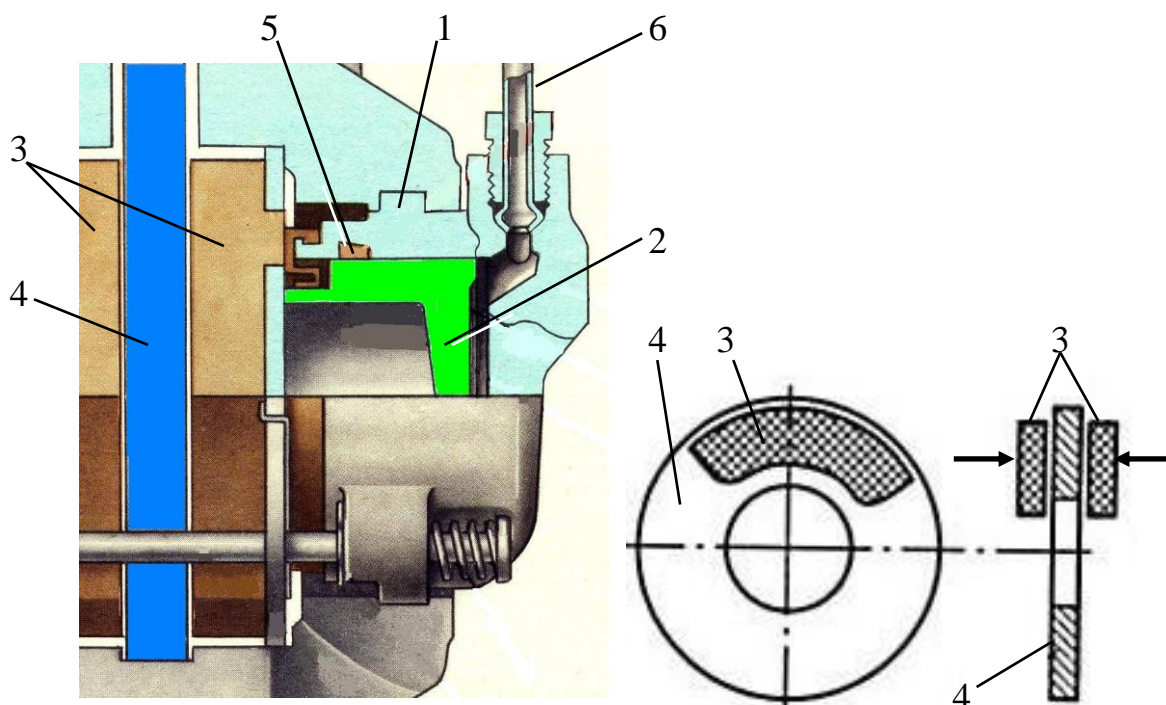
Торможение дискового тормозного механизма: 1 – рабочий цилиндр; 2 – поршень; 3 – накладки тормозных колодок; 4 – тормозной диск; 5 – уплотнительное кольцо; 6 – трубопровод гидросистемы тормозного привода
